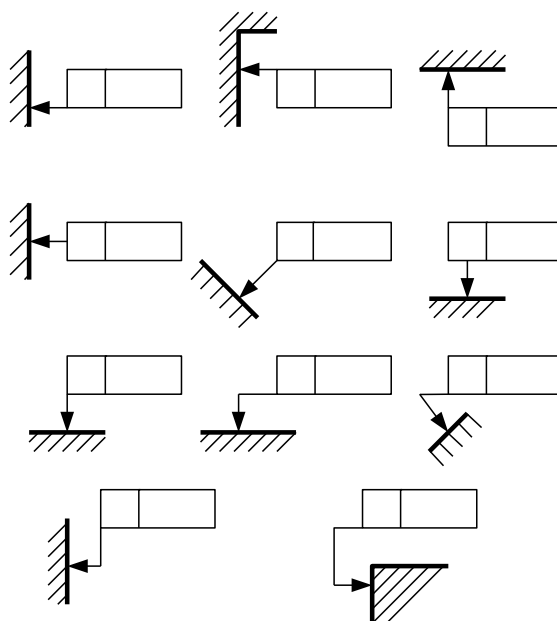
Изображение условных обозначений о допусках формы и расположения поверхностей
